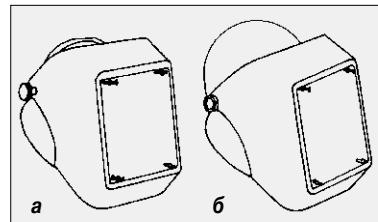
Сварочный щиток с комбинированным светофильтром: а — без каски; б — с каской
